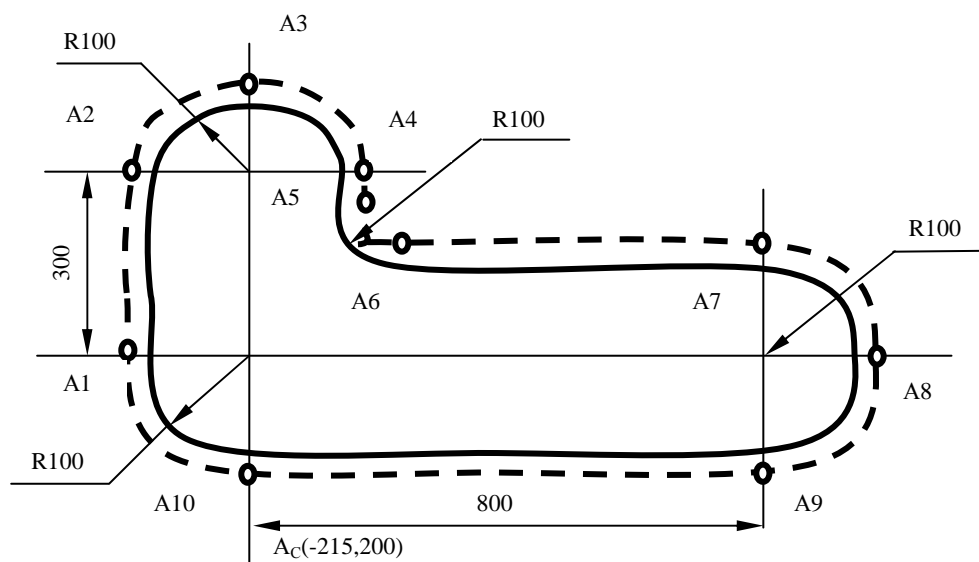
Чертеж детали с коррекцией изменения радиуса фрезы
